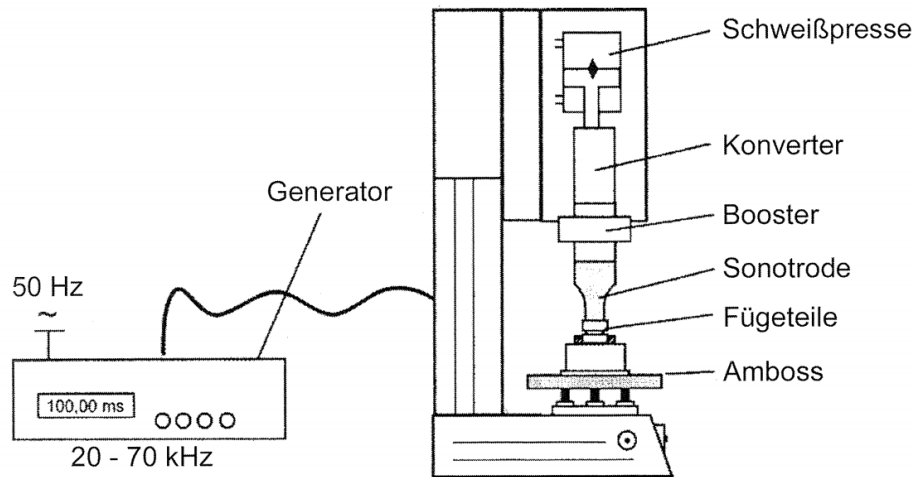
Aufbau und Komponenten einer Ultraschallschweißmaschine (aus [Ehr04])
